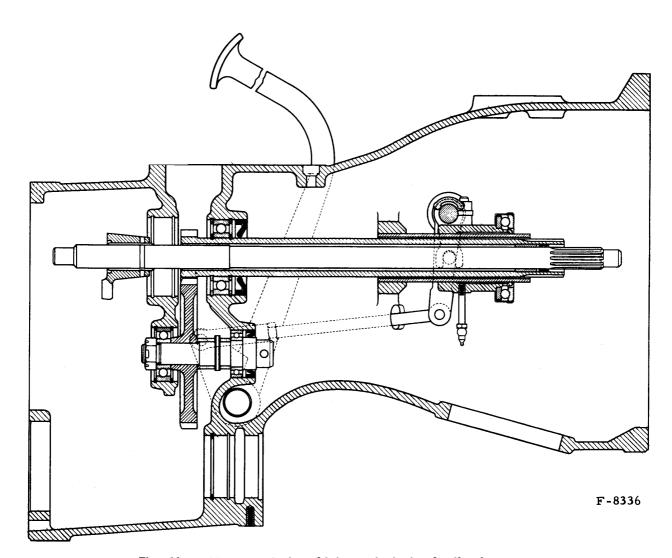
Montage de la pédale et de la butée d'embrayage.
